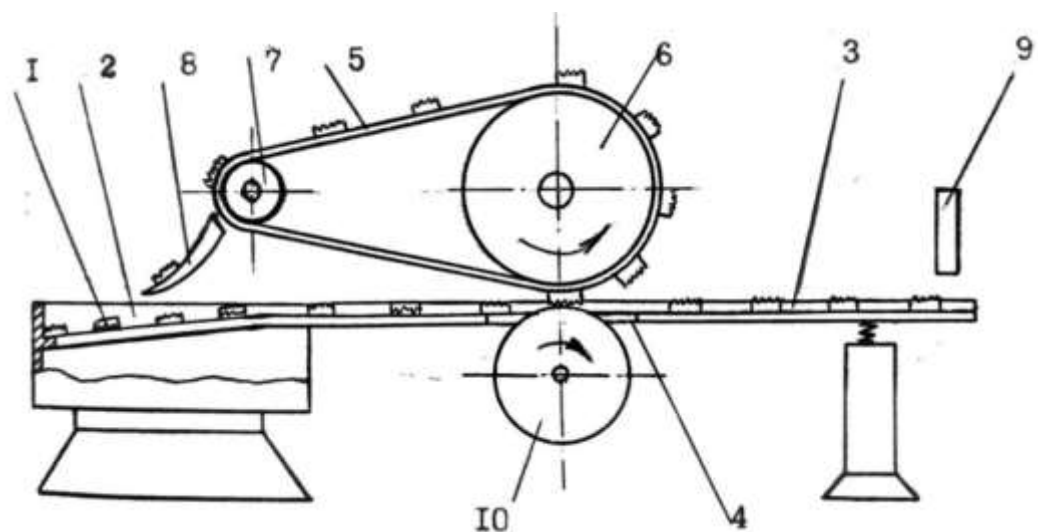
Схема пристрою для орієнтованої подачі деталей із різною шорсткістю поверхонь
